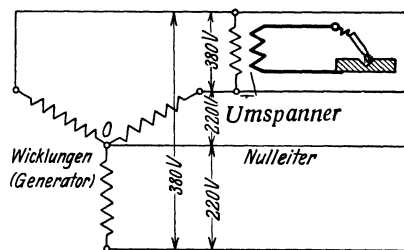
Drehstromsystem in Sternschaltung mit Schweißumspanner zwischen zwei Phasen.
